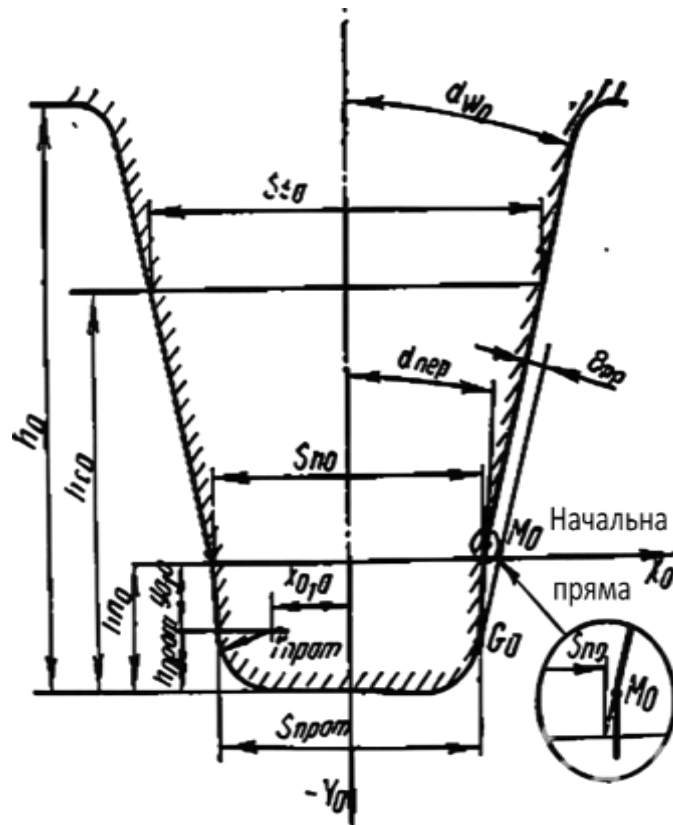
Профіль зуба черв'ячної фрези з протуберанцем
